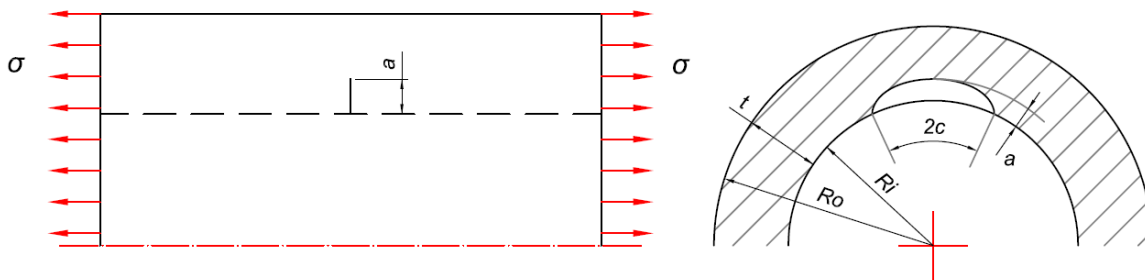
Tubería con fisura semi-elíptica interna en dirección transversal sometida a carga axial.
